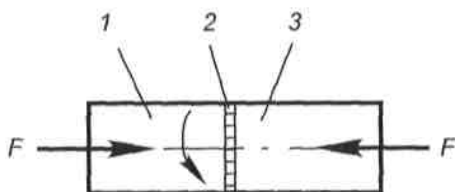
Схема зварювання тертям: 1,3 – заготовка; 2 – зварний шов; F – сила
